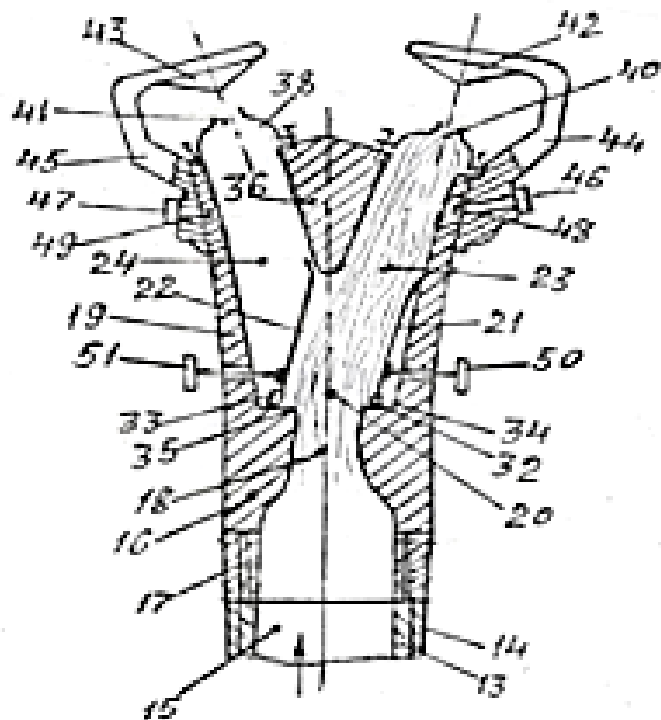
Вариант выполнения струйного усилителя потока в виде вертикальной пластины, связанной стержнем резьбового соединения, ввернутых в резьбу боковой стенки диффузора в упор боковой поверхности стенки вертикальной пластины
